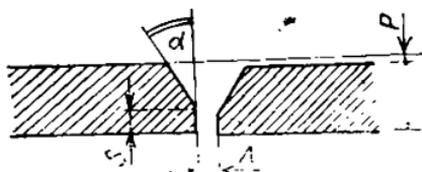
Положение кромок труб в стыке перед сваркой
